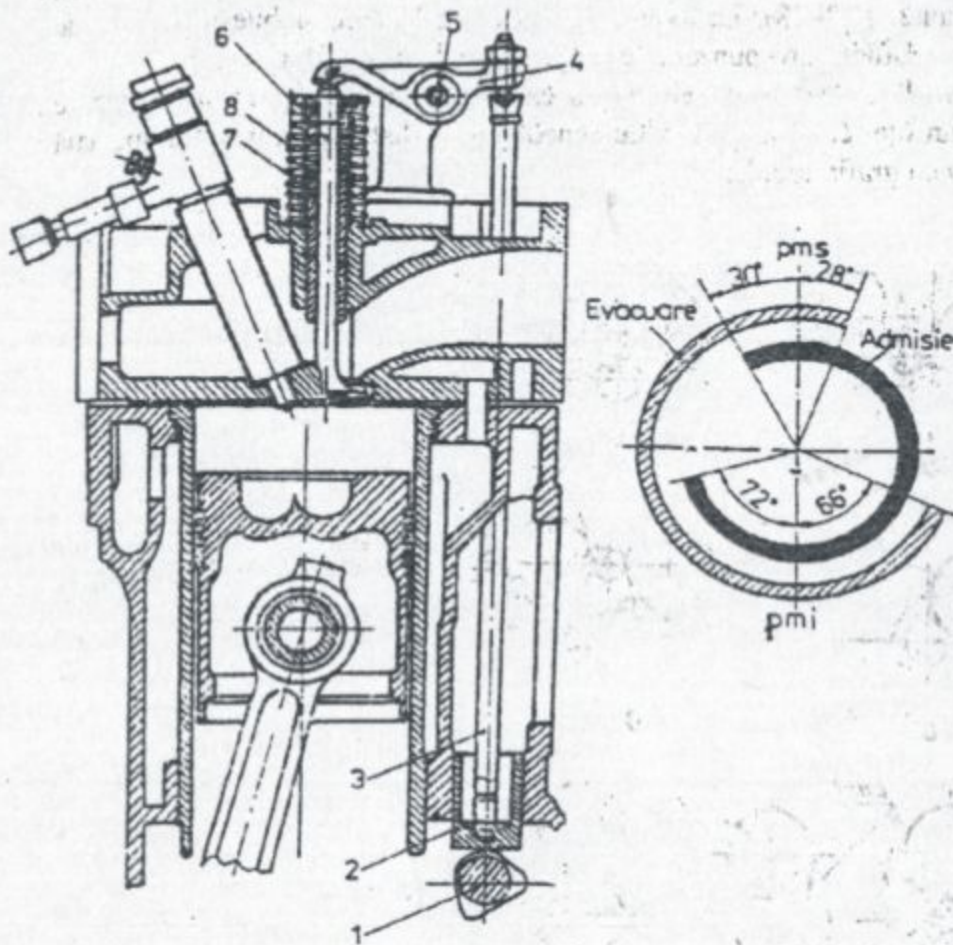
Mecanismul de distribuție a gazelor pentru motorul D-110:
